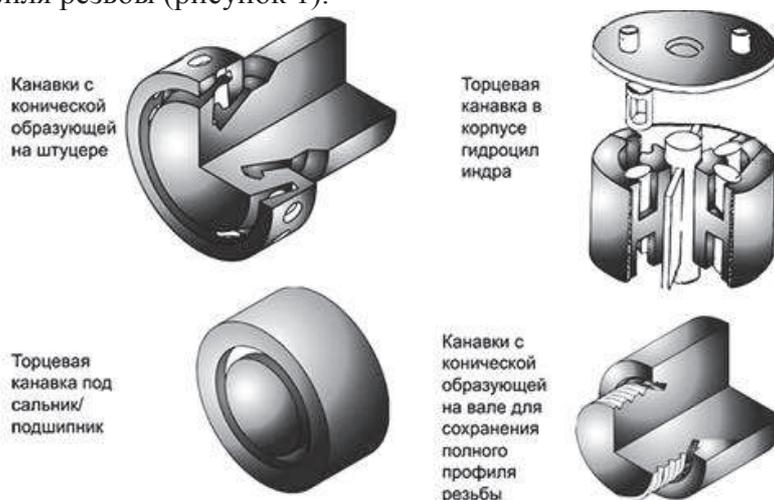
Типовые детали с торцевыми канавками и канавками с конической образующей
